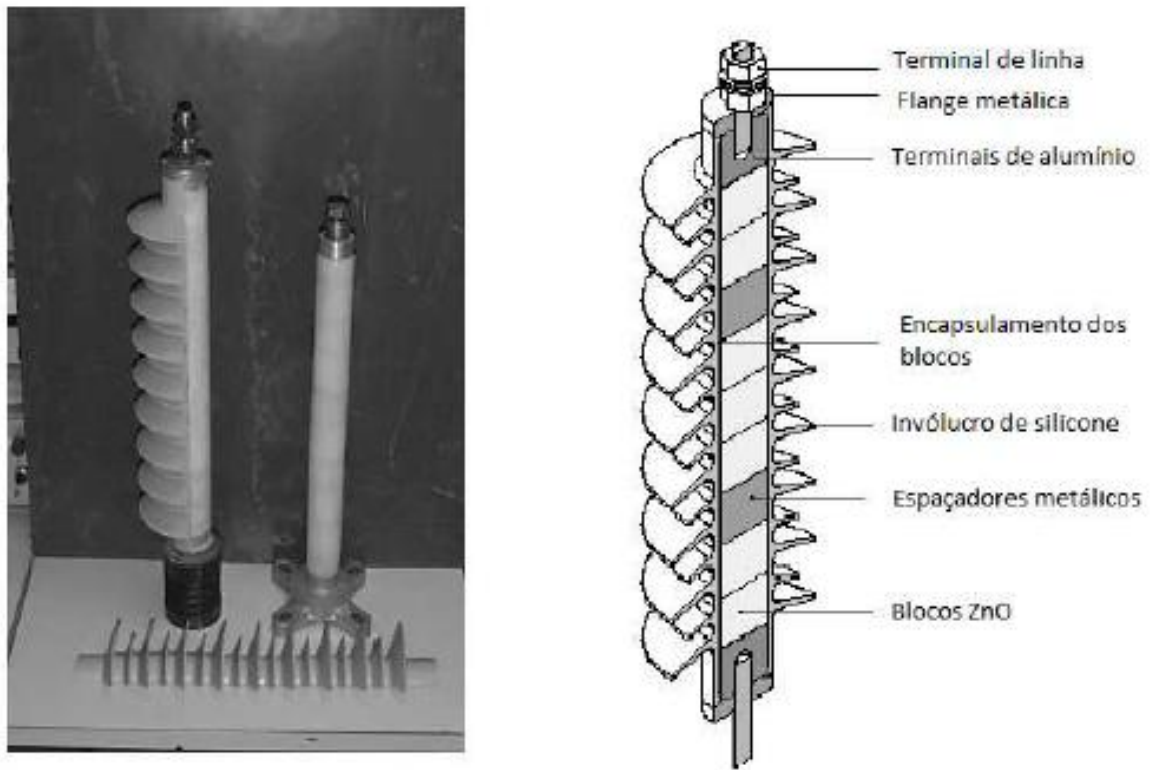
Detalhes do projeto construtivo de para-raios diretamente injetado.
